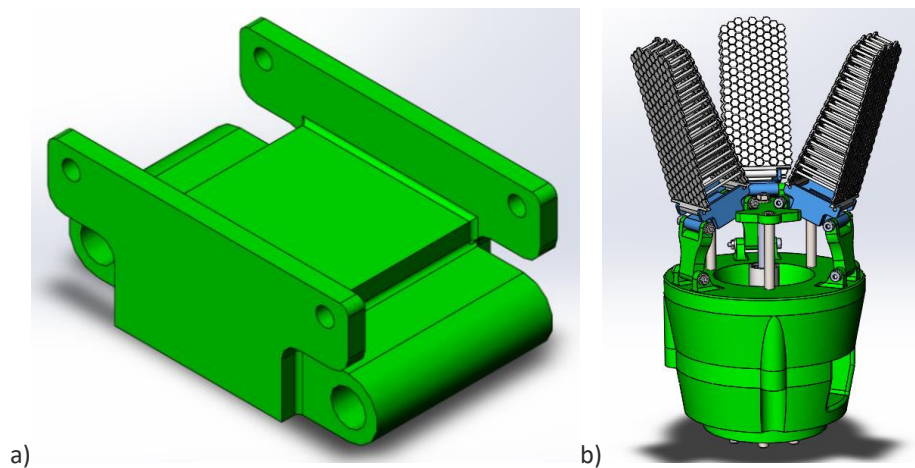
Adaptador - vista do componente (a) e montagem no conjunto (b).
